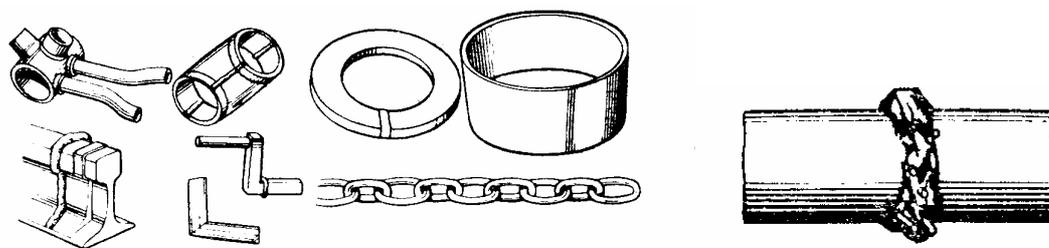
Вид деталей сварного стыкового соединения
